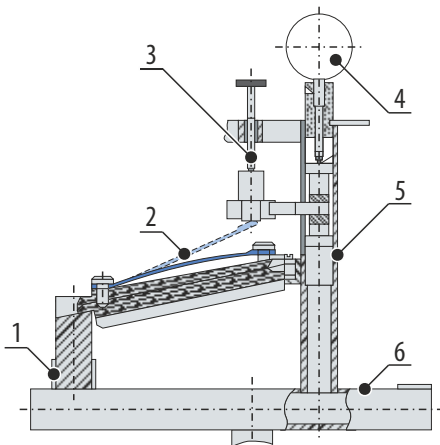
Схема загрузки нагружающего блока с пружиной в измерительное устройство:
